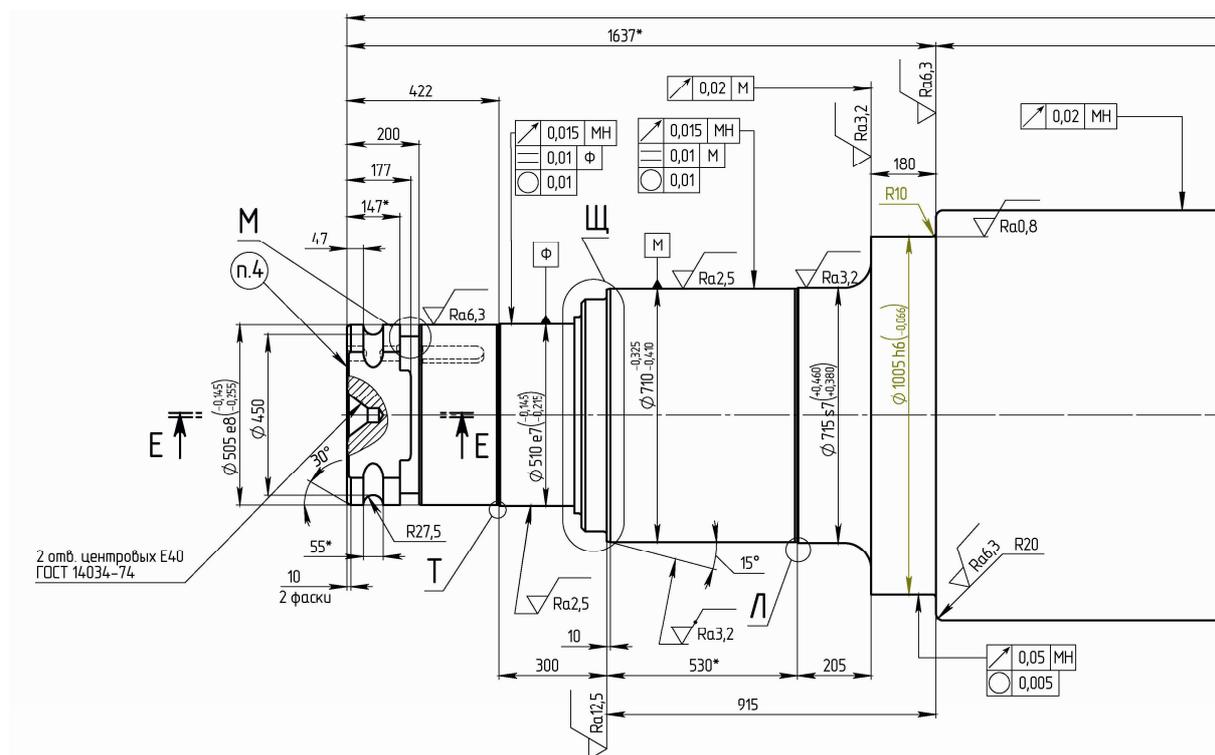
Фрагмент чертежа валка прокатного стана
